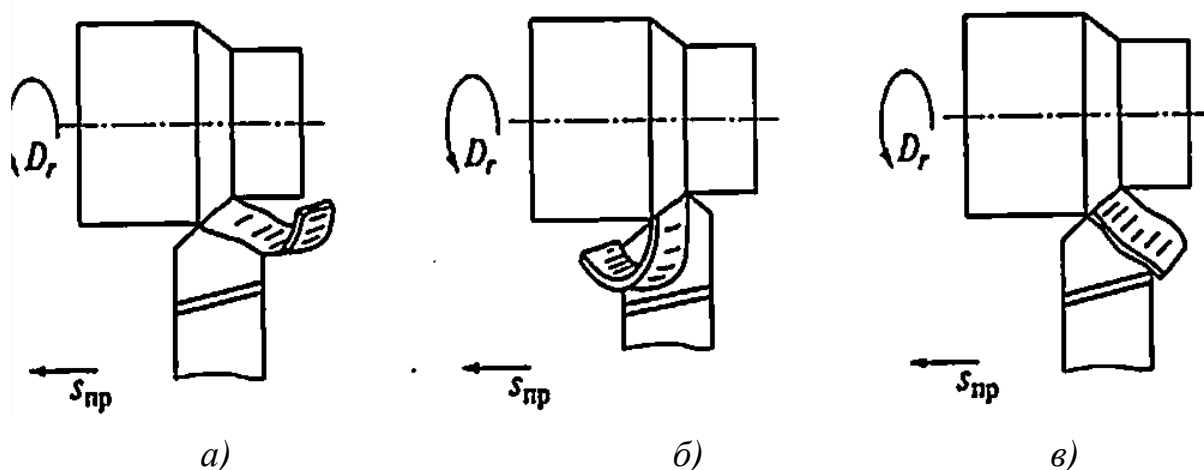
Влияние угла наклона главной режущей кромки на направление схода стружки
